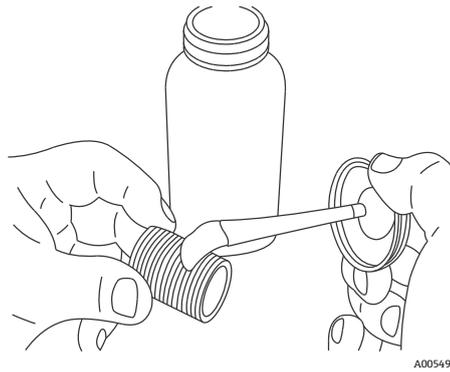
Schmiermittel auf Rohrgewinde aufbringen
